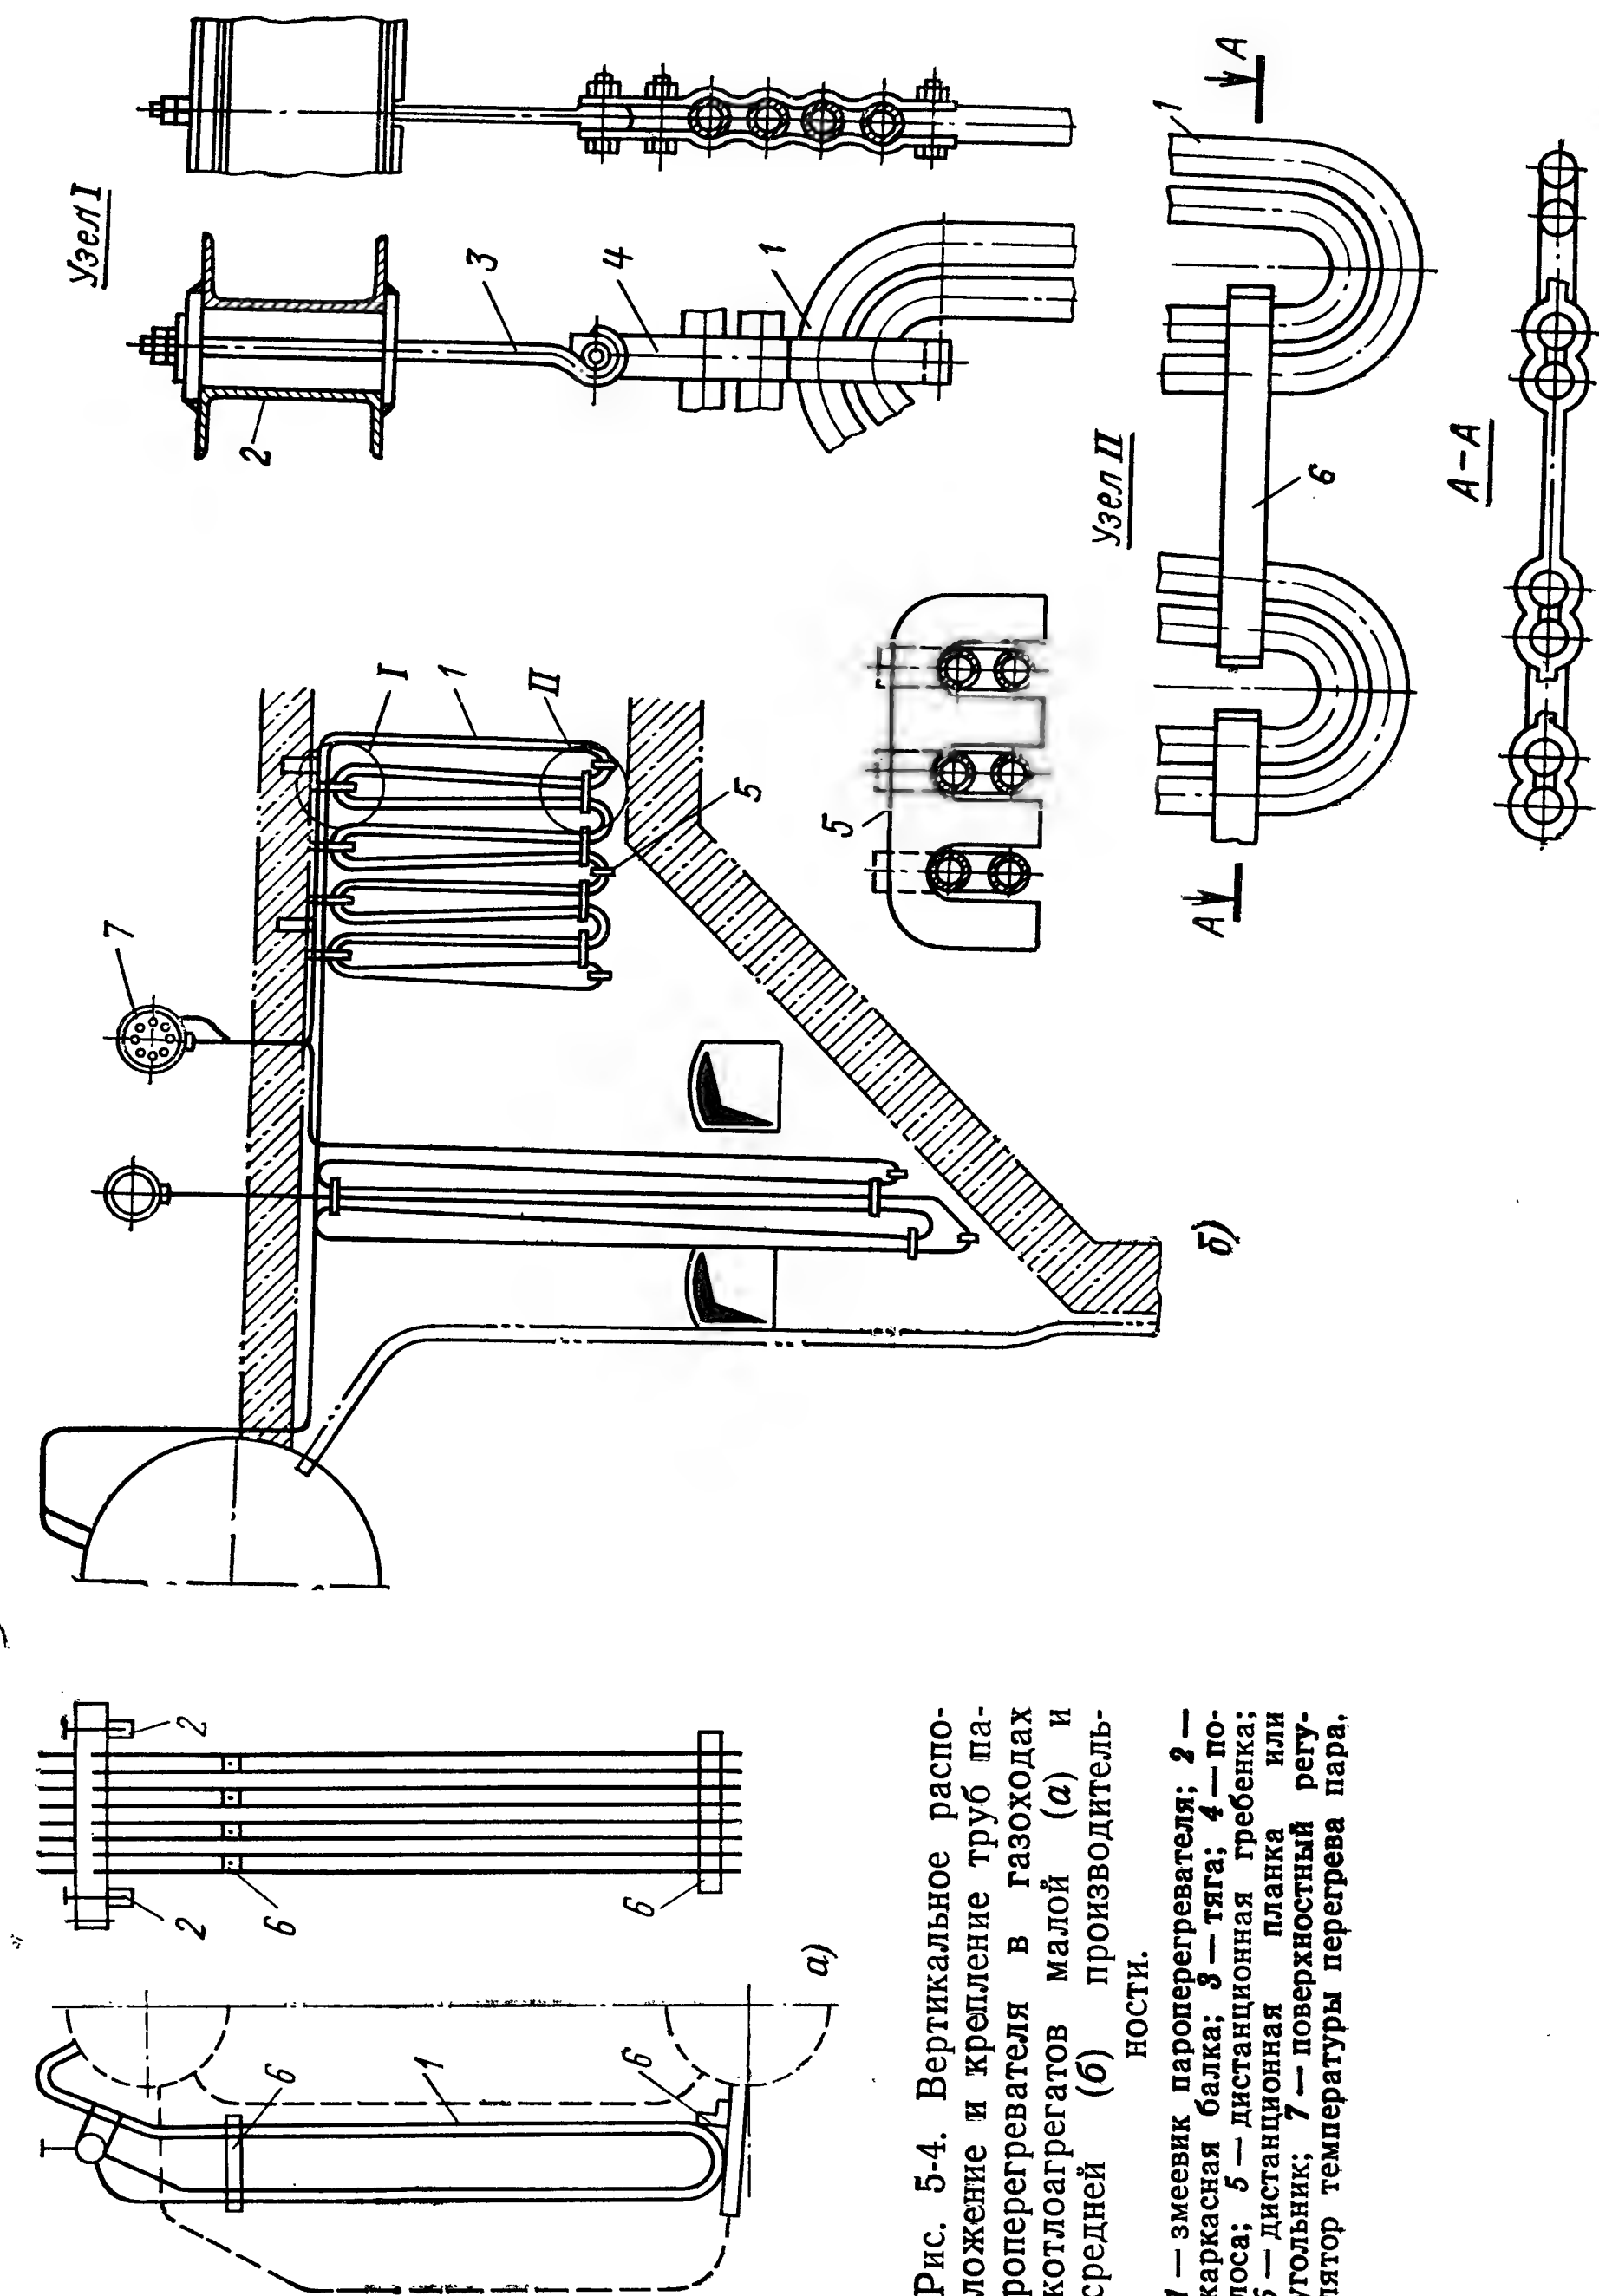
Вертикальное расположение и крепление труб пароперегревателя: 2 — по-
